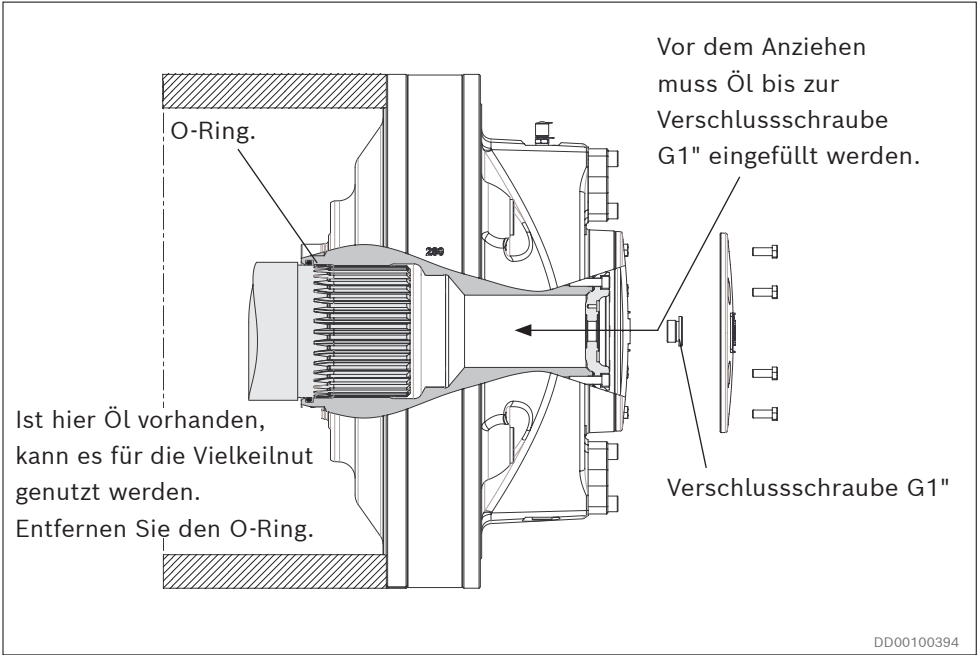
Motor mit Flanschmontage, waagrechte Welle
